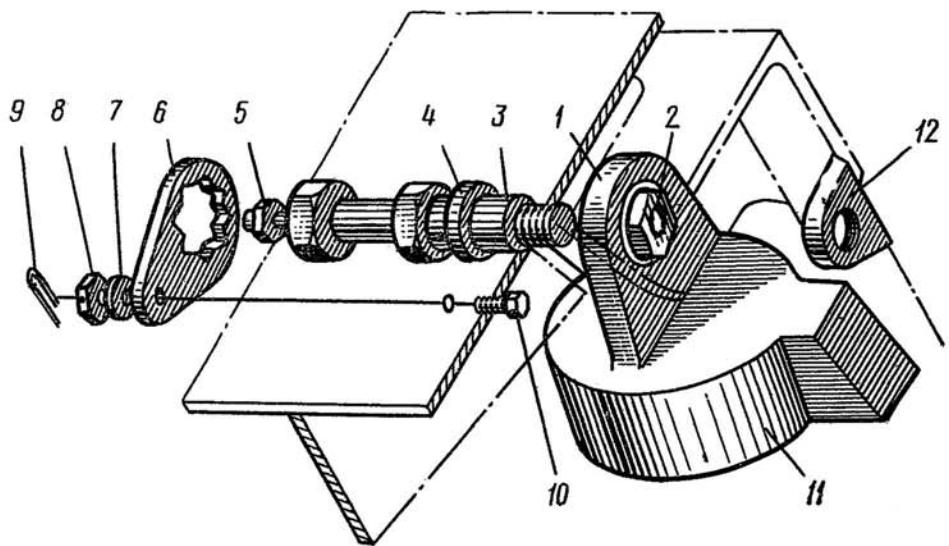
Детали крепления верхней головки силового цилиндра передней опоры самолета:
